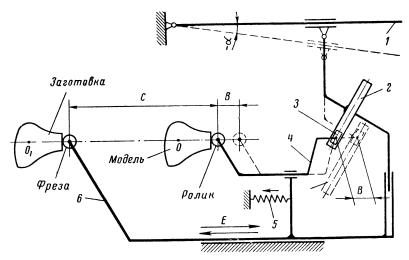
Примерная схема настройки копировально-фрезерного механизма
